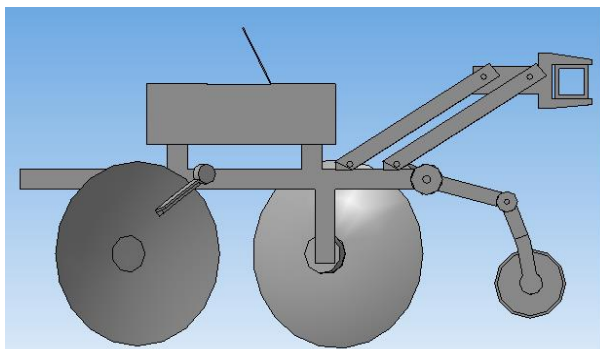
Вид сбоку предлагаемой конструкции окучника
